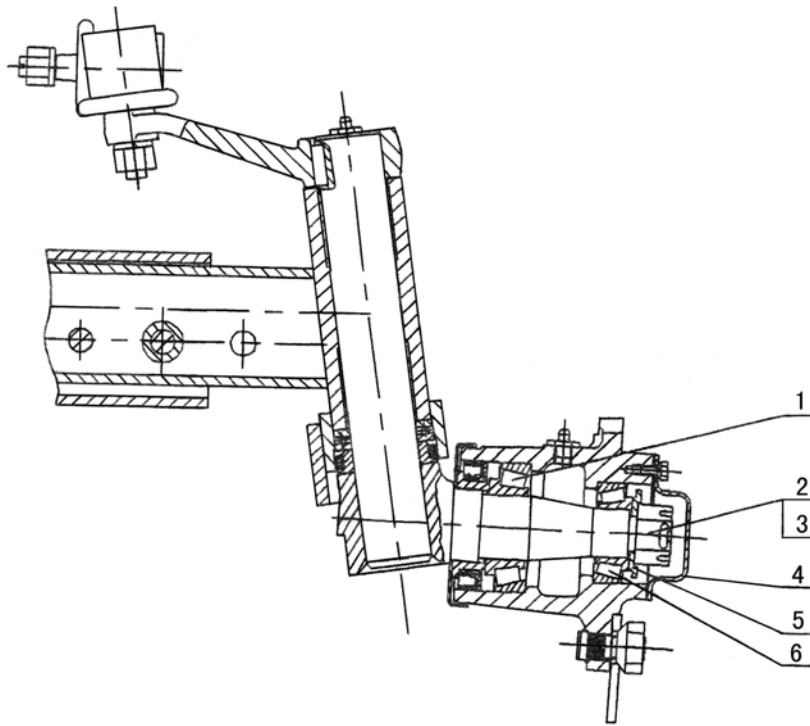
Ajuste de la holgura axial del rodamiento de la rueda delantera
